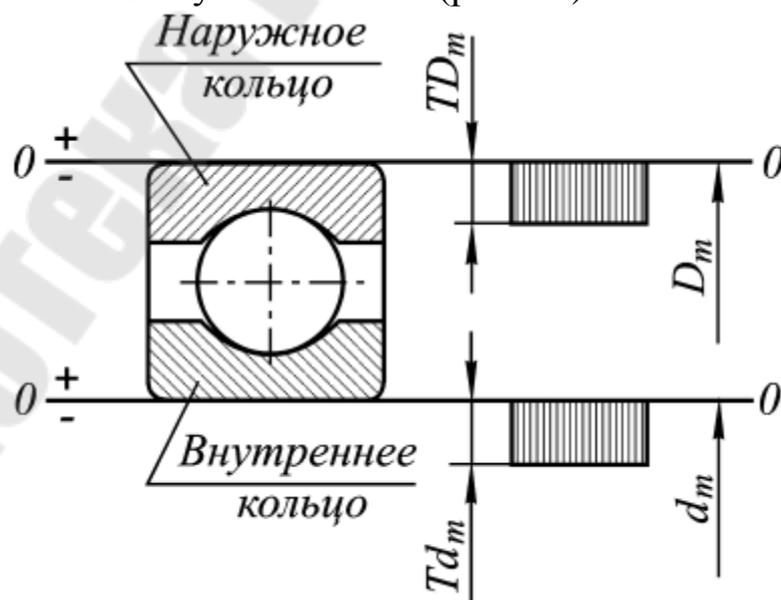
Расположение полей допусков посадочных диаметров колец подшипников
